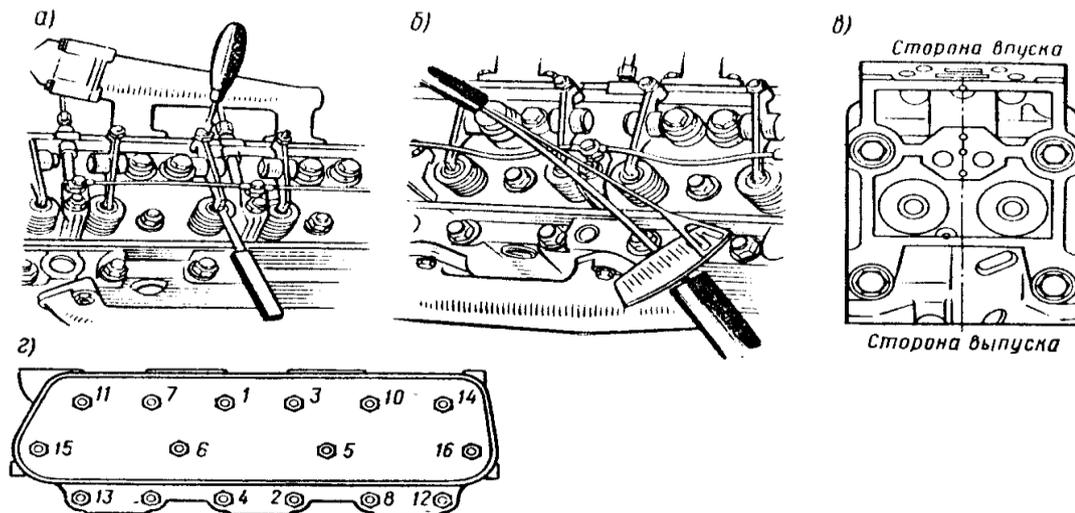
Проверка зазоров в клапанах и креплениях головки цилиндров двигателей;
